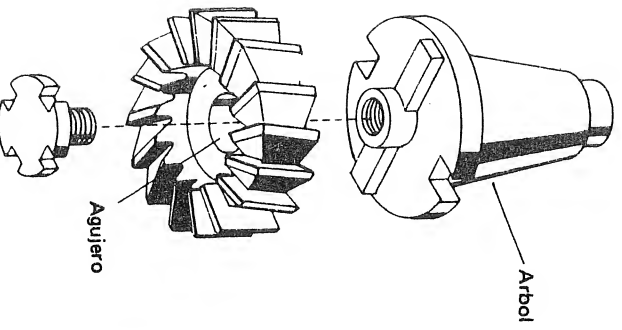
Sujeción de una fresa frontal con agujero de montaje.
